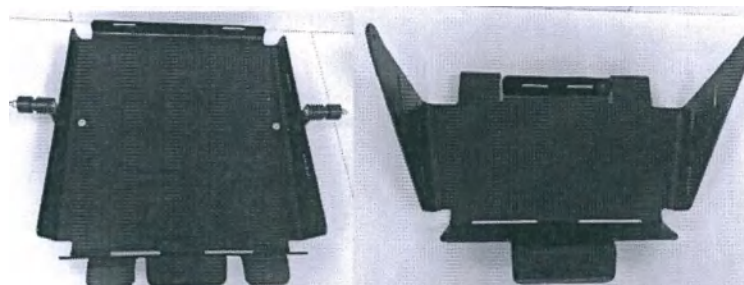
Г. Внешний вид полочки для медицинской аппаратуры: а) для сиденья, установленного в направлении движения; б) для сиденья, установленного против движения.
